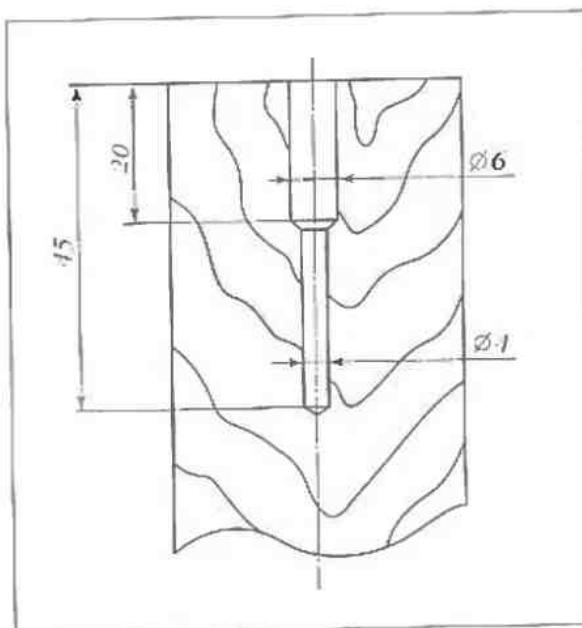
Схема сверления отверстия в заготовке рукояти под остроугольный хвостовик
